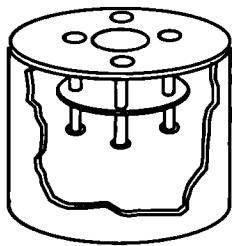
Схема конструкции поршневого цилиндра для гидравлоса
